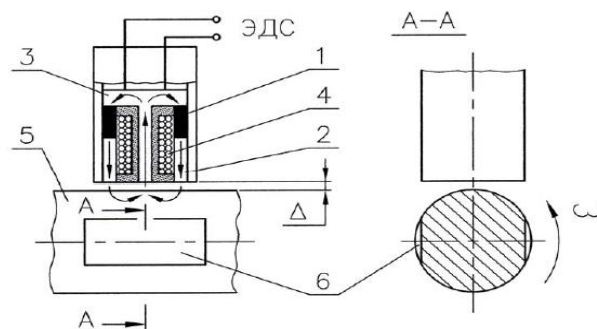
Конструктивна схема індукційного датчика і пристрою для вимірювання частоти обертання валу
